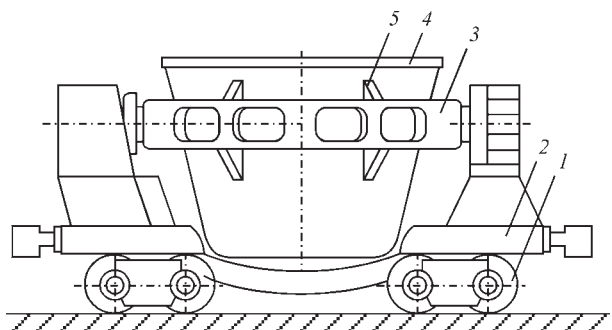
Схема шлаковоза: 1 — ходовая часть шлаковоза; 2 — платформа шлаковоза; 3 — опорное кольцо для чаши; 4 — чаша шлаковоза; 5 — опорные элементы на чаше
